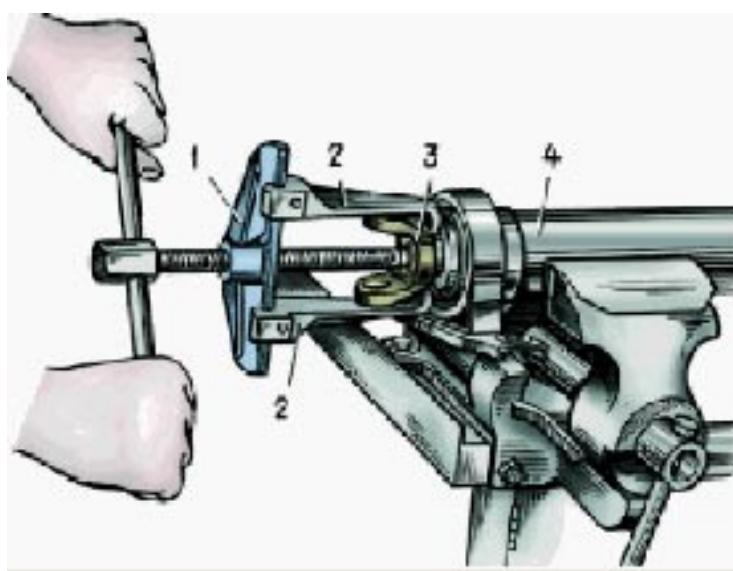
Зняття вилки з переднього карданного вала:
